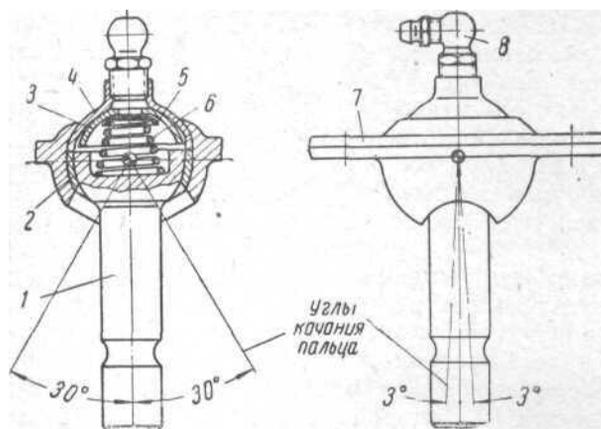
Шаровой шарнир стойки подвески автомобиля модели 407:
